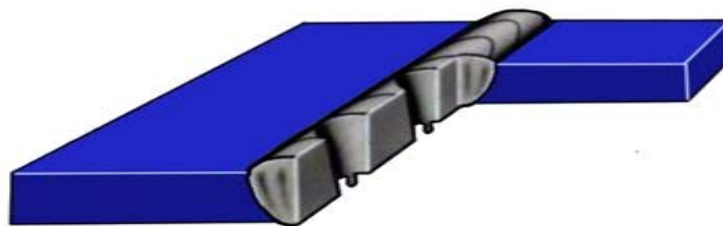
Дефект зварного з'єднання пропал
